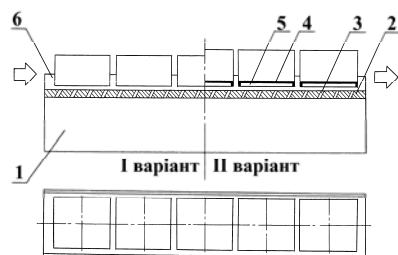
Неприводний конвеєр на повітряній подушці з нахиленими циліндричними каналами: 1 - ресивер; 2 - сопловий пристрій; 3 - канал; 4 - піддон; 5 - пазуха; 6 - спрямовуючий борт
